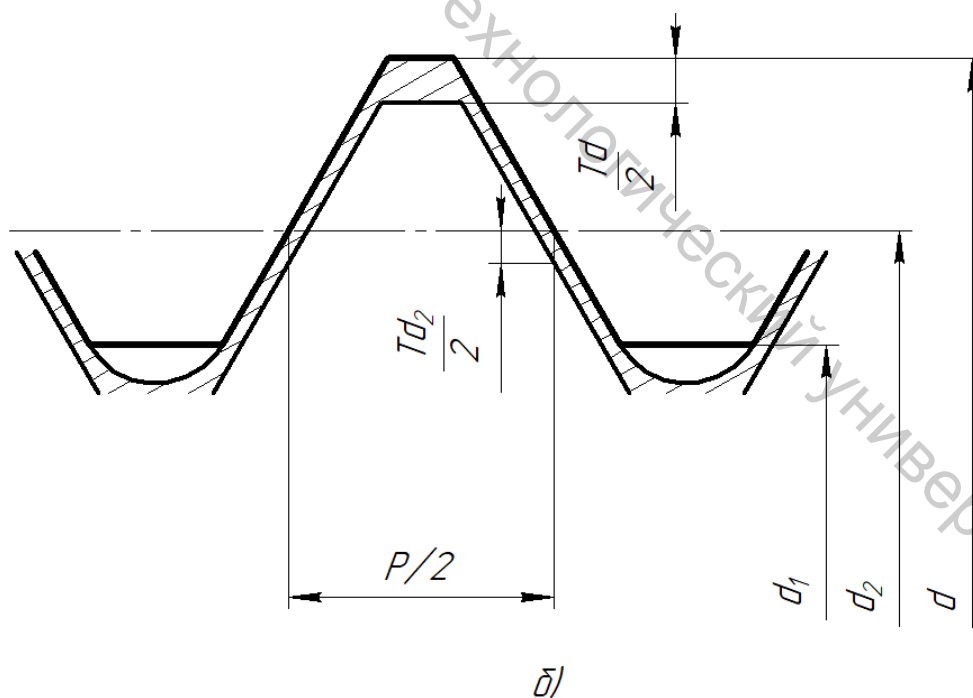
Расположение интервалов допусков наружной резьбы
